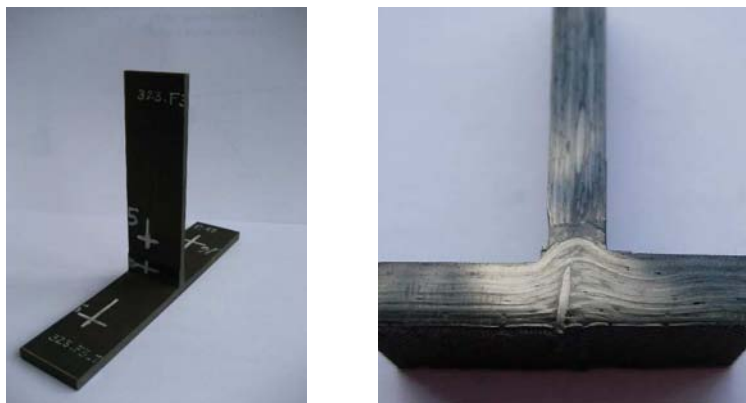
Eprouvette en T avec clous de 40 mm sur trois lignes (gauche) et détail de la liaison peau/voile sans semelle (droite)
